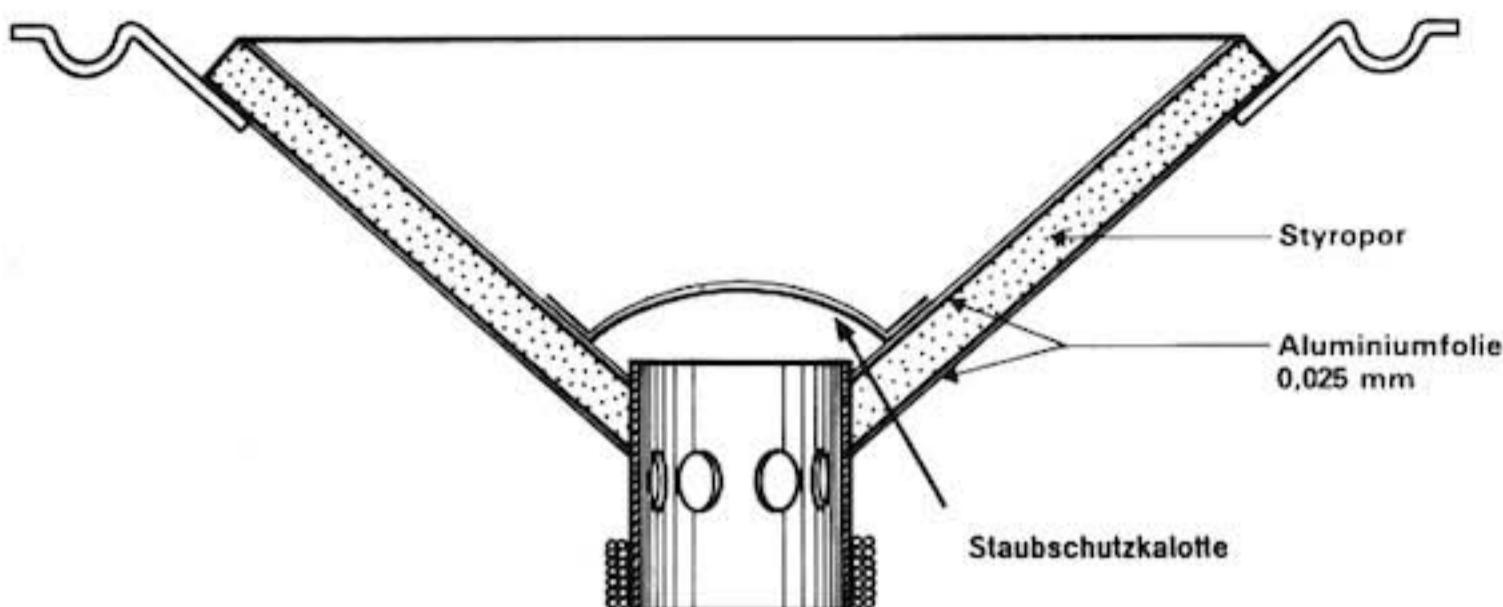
Der typische Aufbau einer Styropor-Membran.
